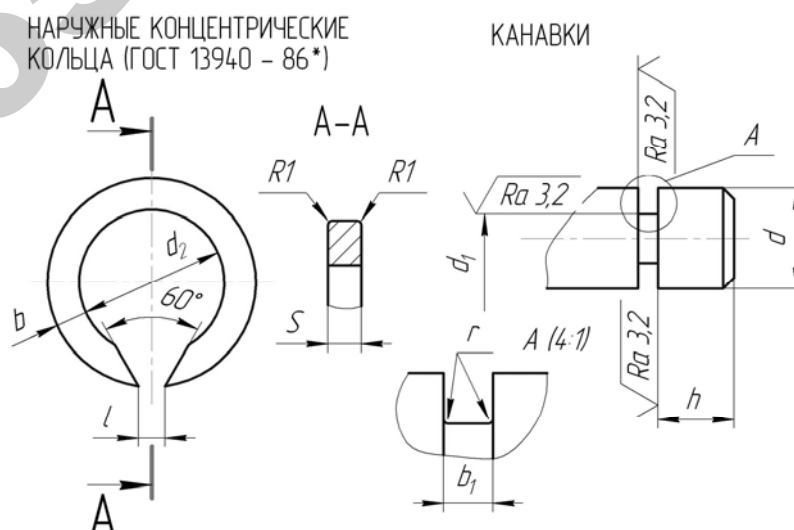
Форма и размеры канавок под наружные концентрические кольца
